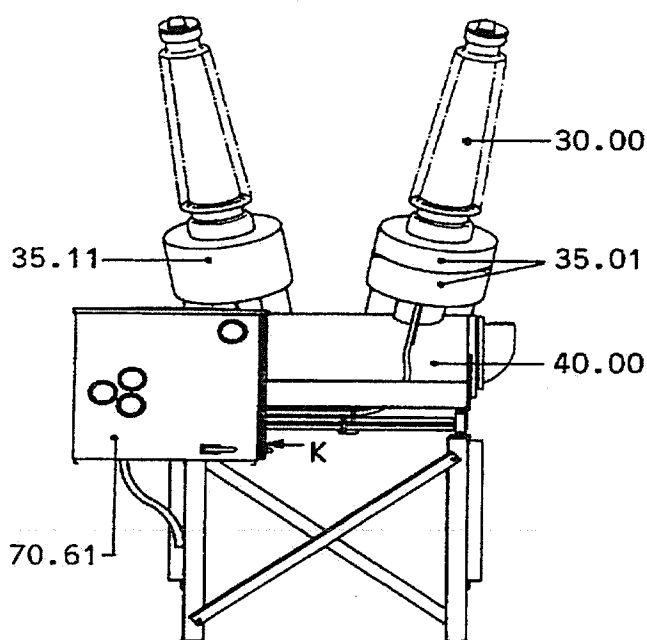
В: Общий вид выключателя (вид со стороны шкафа Привода)
